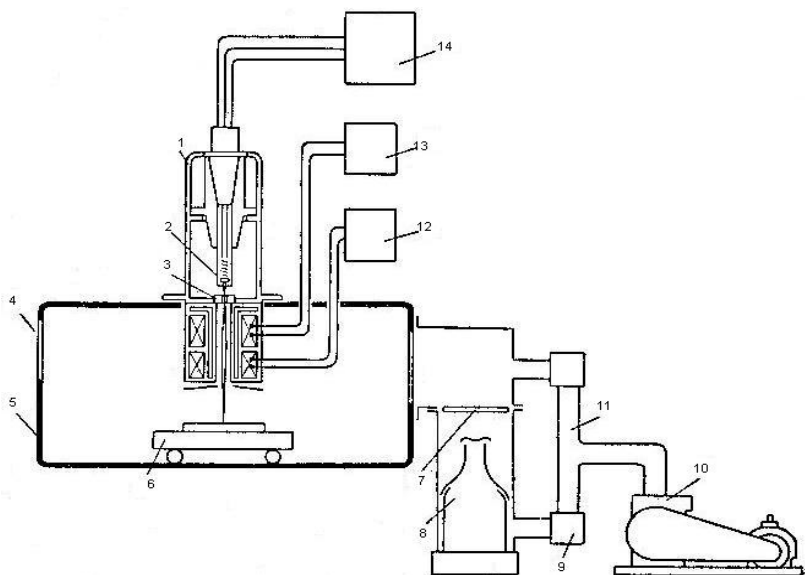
Схема установки для электронно-лучевой сварки:
